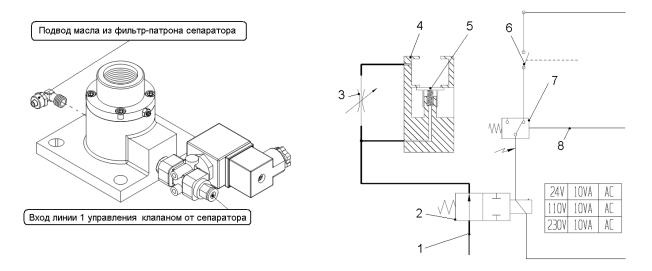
Схема управления впускным клапаном: 1 – линия управления от сепаратора; 2 - минипневмораспределитель с электроуправлением; 3 – дроссель разгрузки; 4 – корпус клапана впускного; 5 – тарелка; 6 – выключатель; 7 – датчик давления; 8 – линия управления от потребителя.
